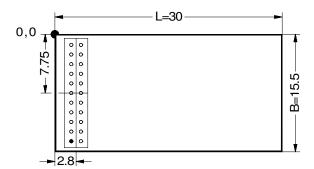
Decoder mit Buchsen-Leiste, Draufsicht
